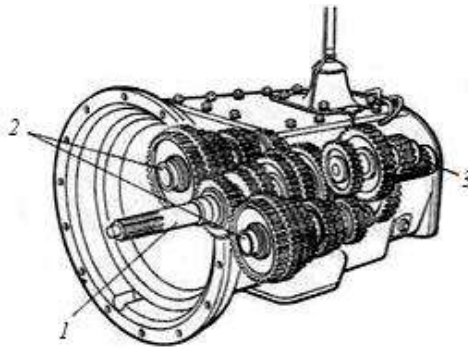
Коробка передач з двома проміжними валами вантажного автомобіля: 1–3 – вали відповідно ведучий, проміжний і ведений
